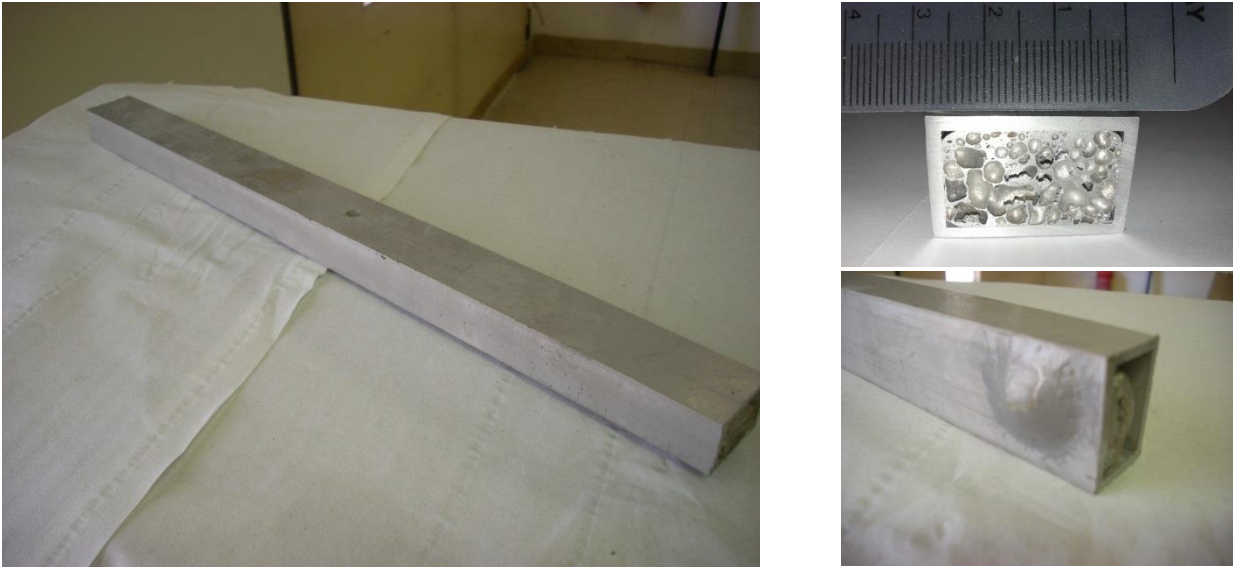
Profilato estruso di lunghezza 400 mm con evidenza della zona di collasso per eccessiva vicinanza alla parete posteriore del forno
